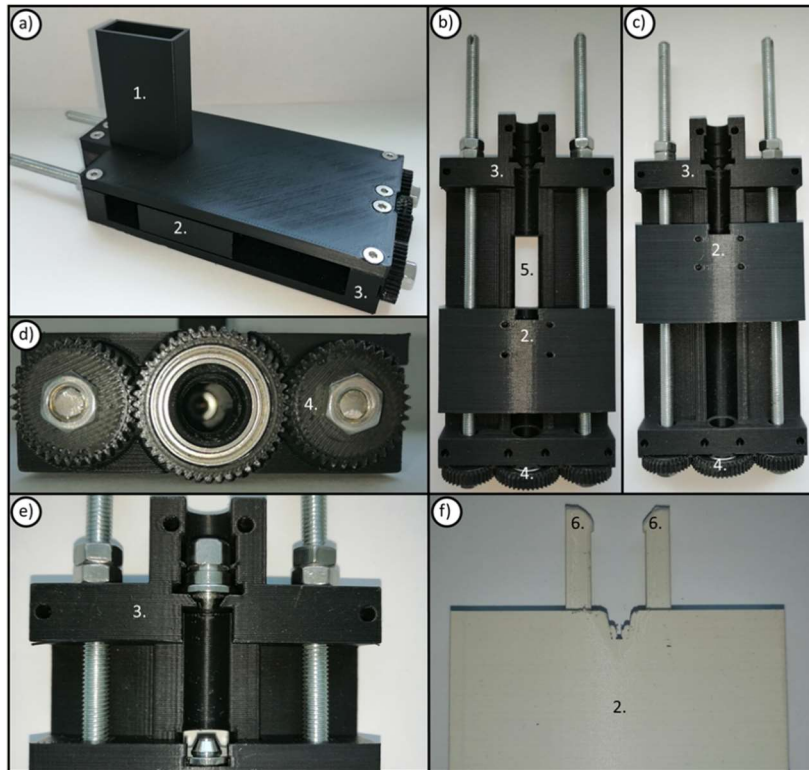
Bilder des Kartuschenwechslers. a) Ansicht des montierten Wechslers. b) Wechsler ohne Deckel in geöffneter Position. c) Wechsler ohne Deckel in geschlossener Position. d) Seitenansicht des Getriebes. e) Wechsler mit eingesetzten HPLC-Anschlüssen. f) Alternativer Kartuscenträger mit Clips. 1. Magazin und Deckel; 2. Kartuscenträger; 3. Wechslergehäuse 4. Zahnräder 5. Kartuschenauswurf; 6. Klammern.
